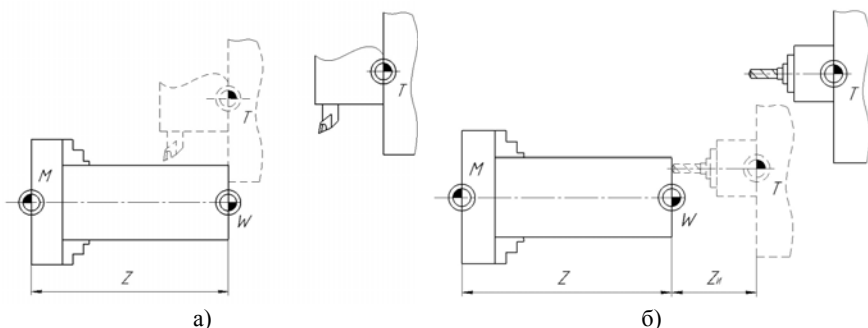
Определение нулевой точки заготовки W способом «касания» посредством револьверной головки (а) и режущего инструмента (б)
